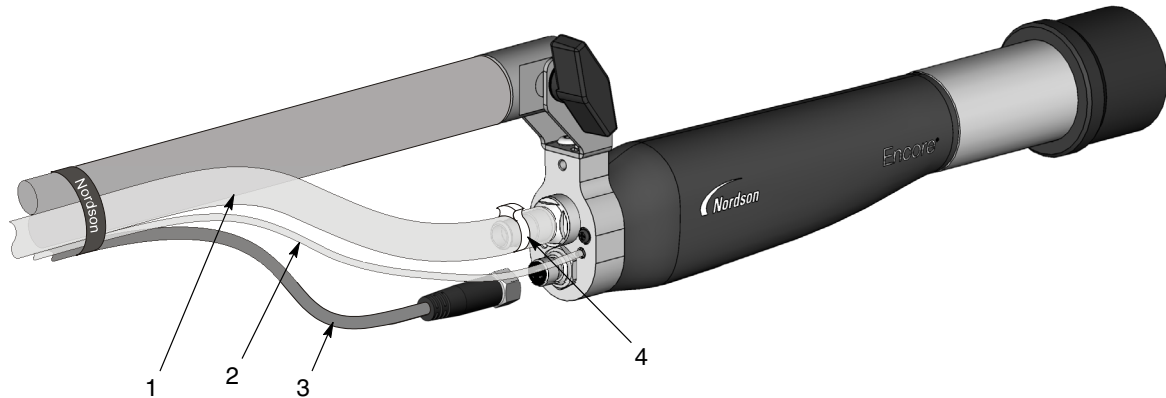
Opcjonalne zestawy montażowe pistoletu do poręczy
